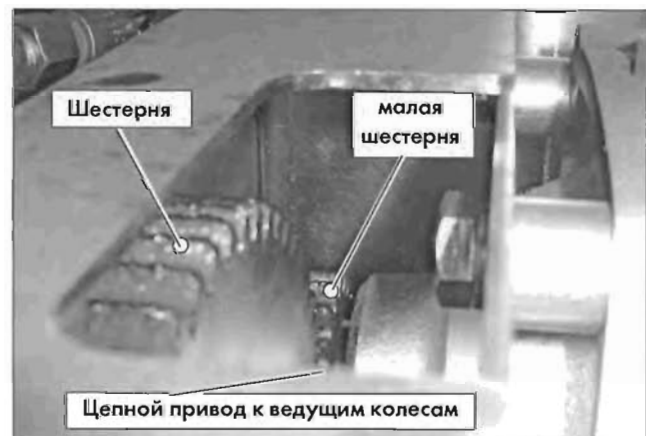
Обслуживающее отверстие в корпусе редуктора (корпус редуктора подачи)
